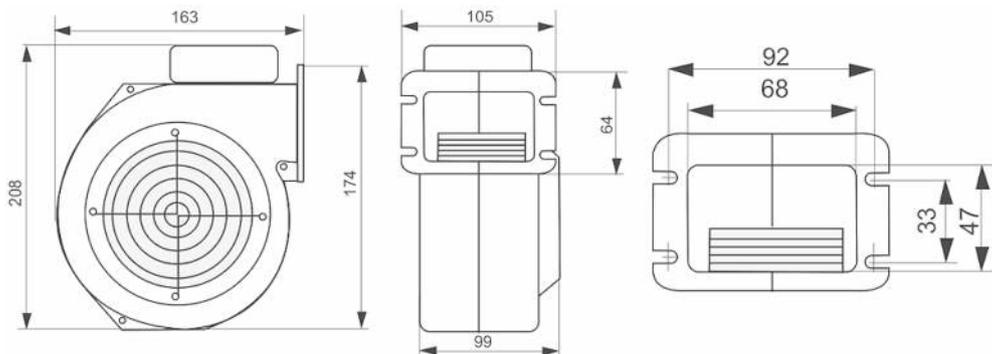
Габаритные и присоединительные размеры вентилятора наддува
